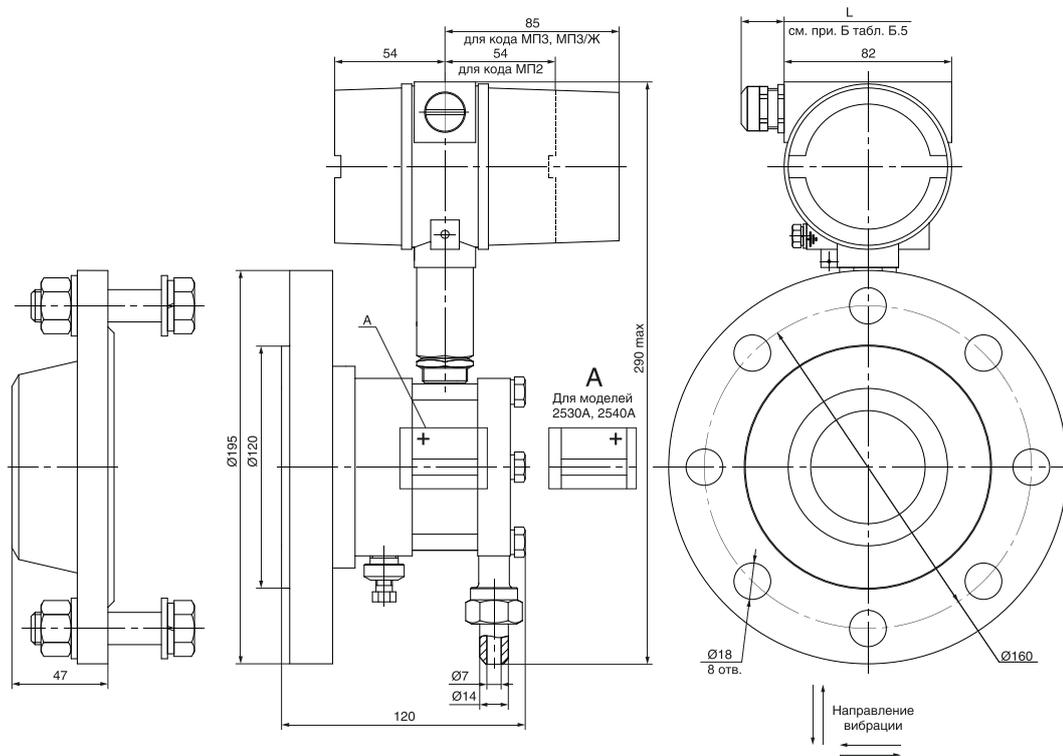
Датчики специального фланцевого конструктивного исполнения моделей 2530, 2540, 2530А, 2540А. Соединение и развальцовка трубопровода $\varnothing 7$ по ГОСТ 13954-74. Фланец присоединительный для установки датчика на стенке резервуара по ГОСТ 12815-80 исп. 3 (ряд 1), PN = 4,0 МПа, DN = 80 мм. В комплекте с фланцем паронитовая прокладка Б-80-100 ПОН по ГОСТ 15180-86
